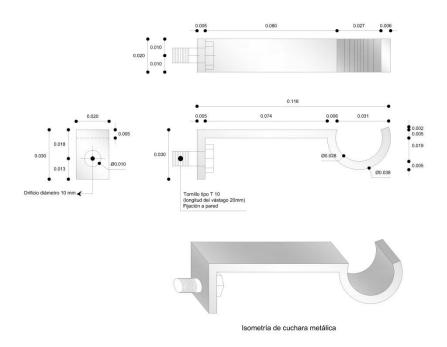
Detalle de cuchara metálica (sujeción para tubería de riego). Fuente: Eduardo Rivadeneira
